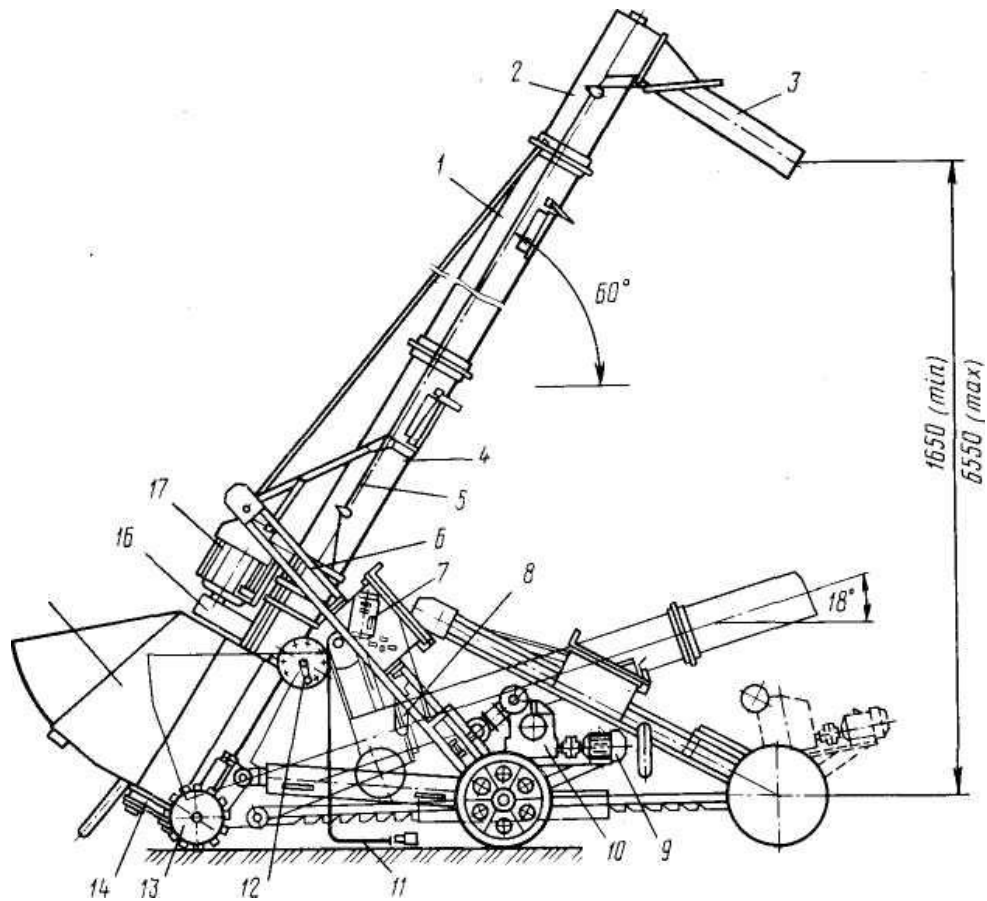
Пересувний самохідний шнековий робочий орган
